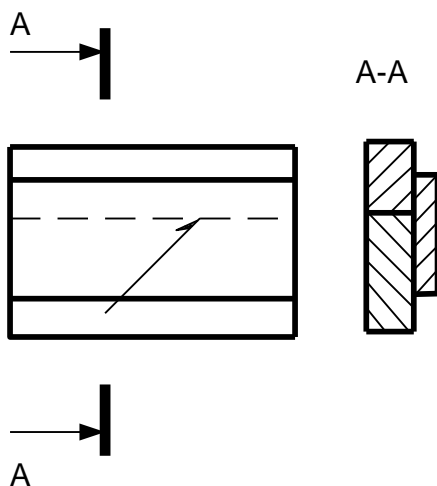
Изображение невидимого шва сварочного соединения
